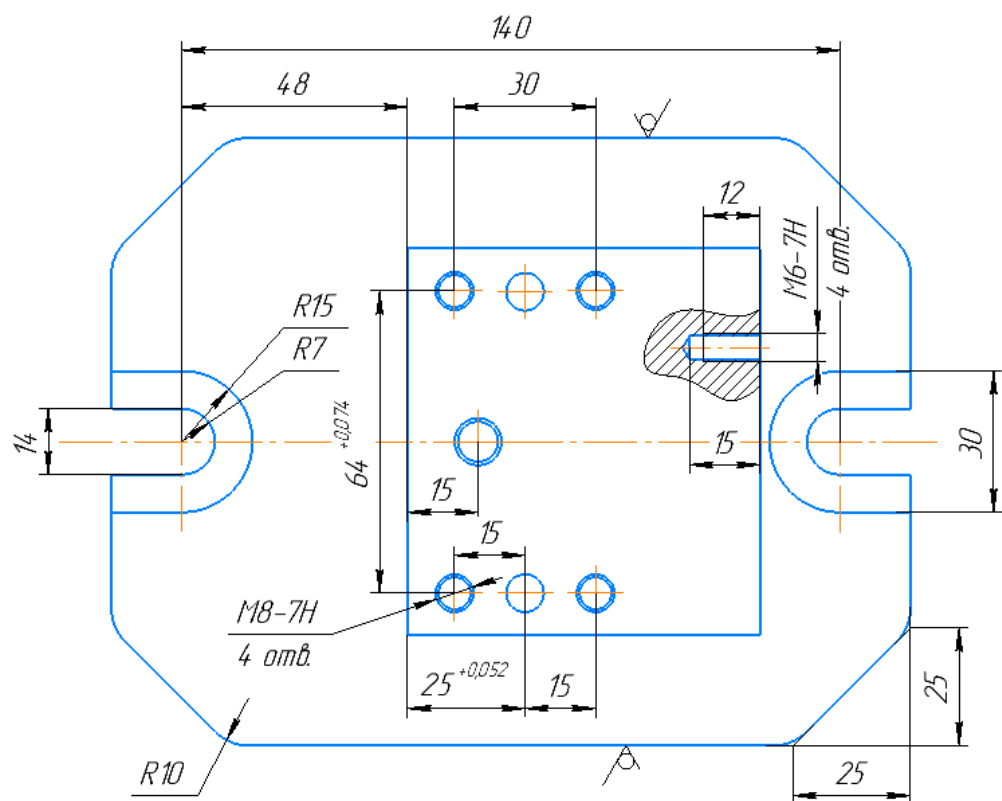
Чертеж детали 2 до метрологической экспертизы (вид сверху)
